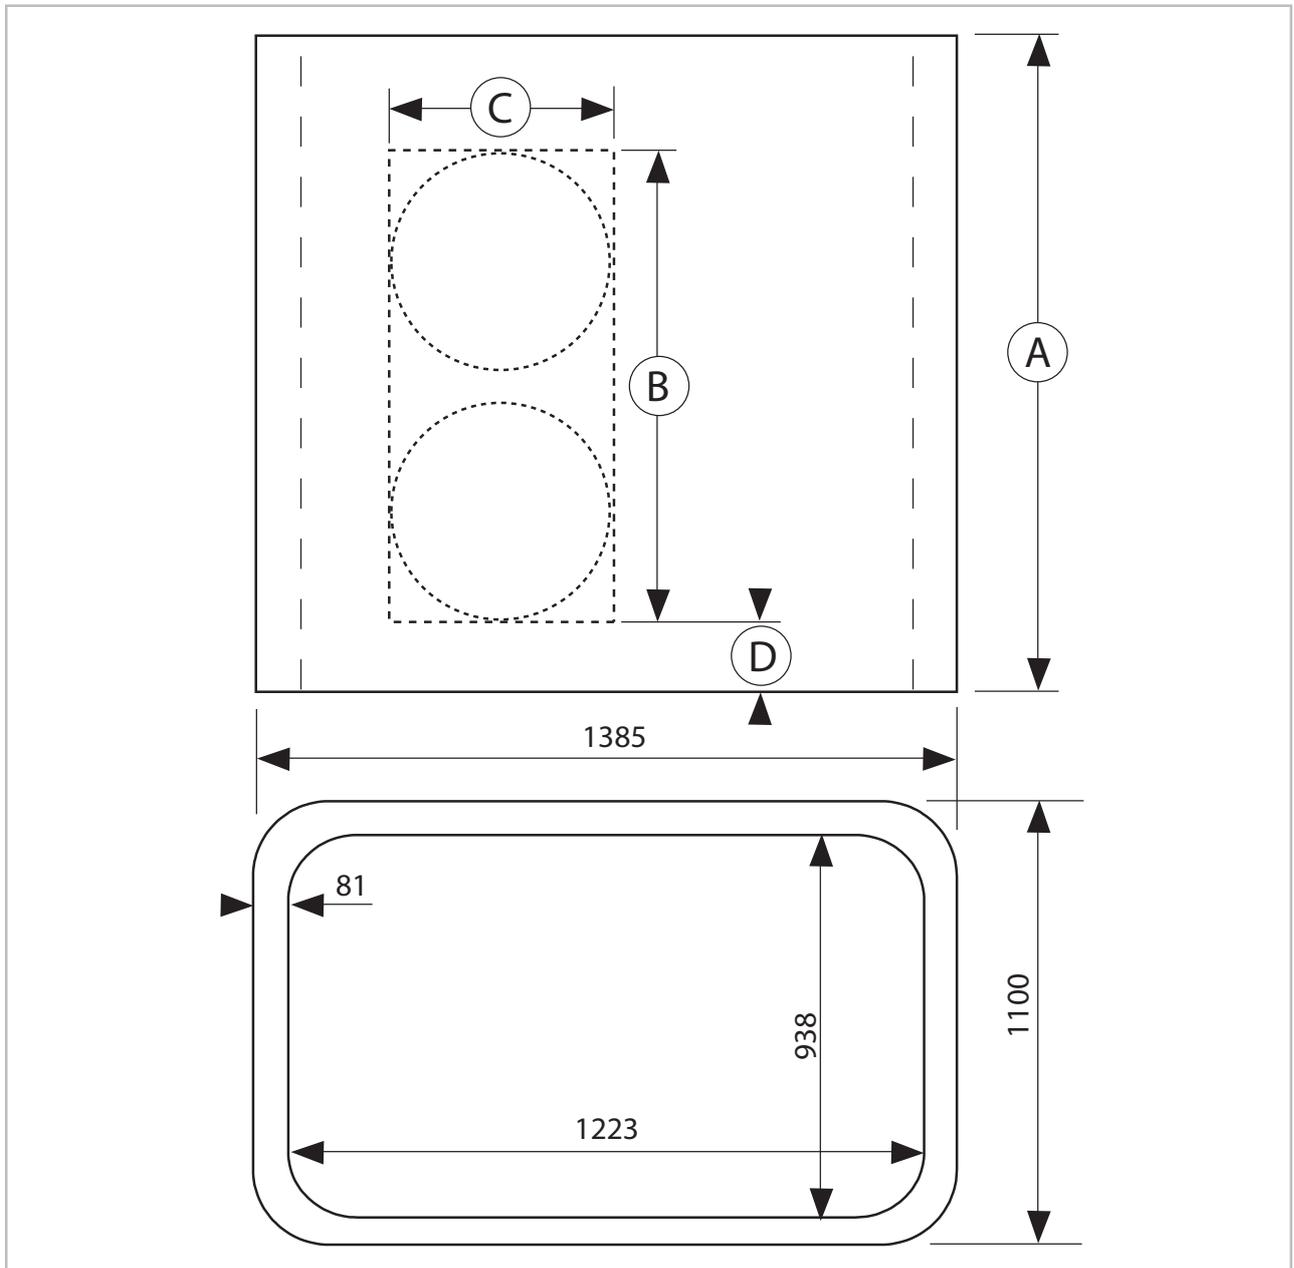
Abmessungen Schallschutzhauben (Alle Maße in mm)
